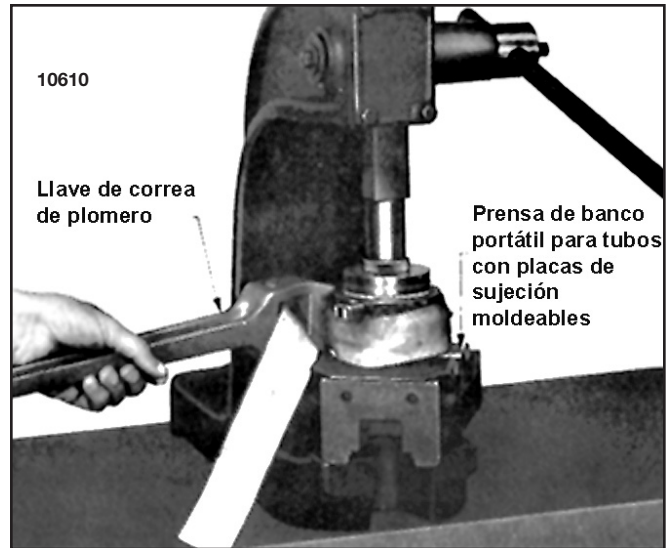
Enrosca el engranaje del freno de carga usando una llave de correa para colocar el resorte del freno de carga
